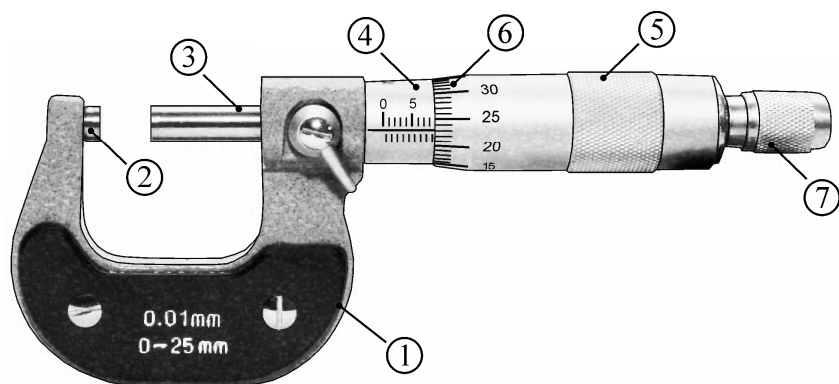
Зовнішній вигляд та будова мікрометра: 1 – сталева скоба; 2 – опорна п'ята; 3 – мікрометричний гвинт; 4 – гільза з внутрішнім різьбленням; 5 – барабан; 6 – додаткова шкала; 7 – ручка тріскачки
